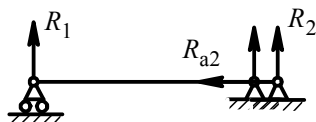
Схема установки вала на одной плавающей и одной фиксирующей опоре с двумя подшипниками в ней
